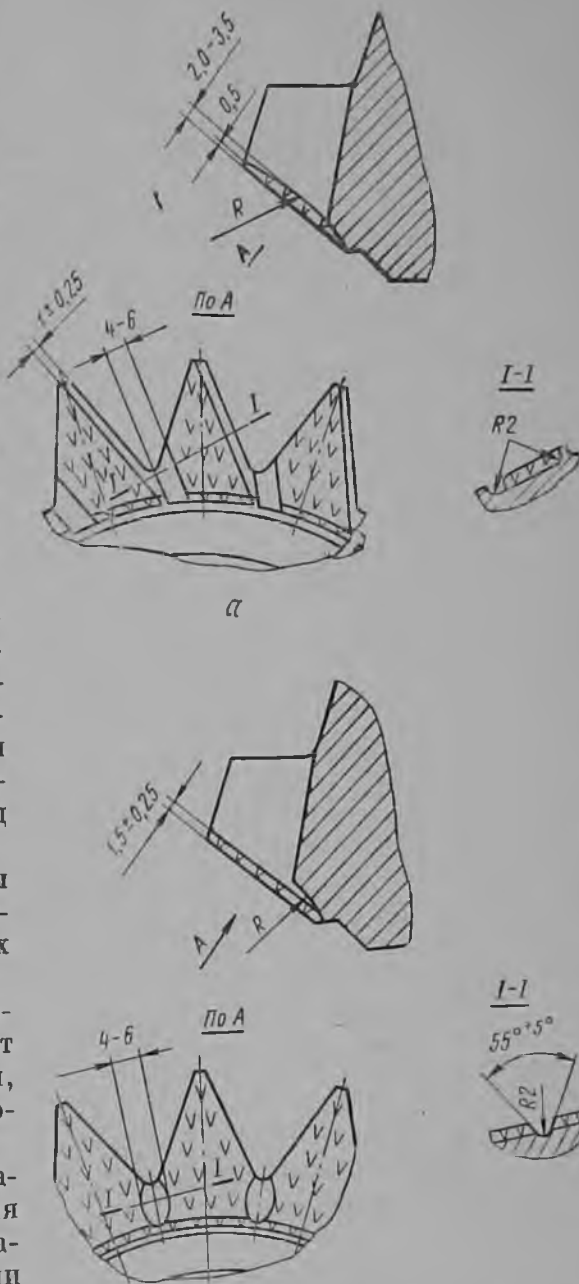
Схемы армирования и разделки тыльной части шарошек. а — для газовой наплавки; б — для наплавки ТВЧ.
